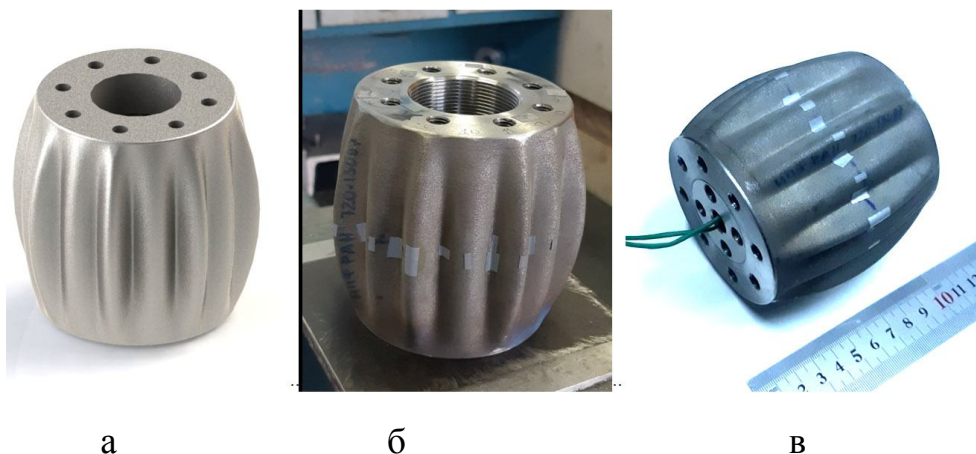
STL-модель корпуса (файл-проект для 3D-печати) (а), цельнометаллический корпус (б) и внешний вид собранного 3D НЧИ (в)
